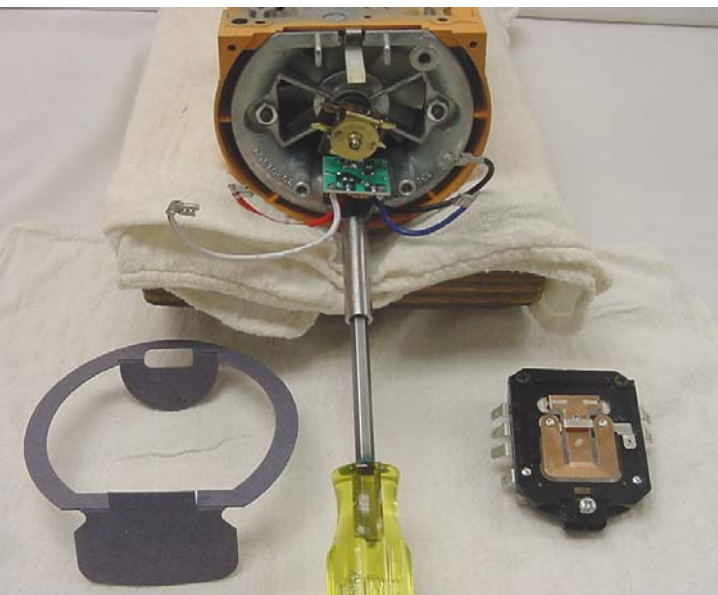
Triac wird an der Lagerbrücke befestigt. ACHTUNG: Phasensteuerung nicht zu fest anschrauben. Zu hoher Druck kann den Kühlkörper verformen und die Steuerung beschädigen.
